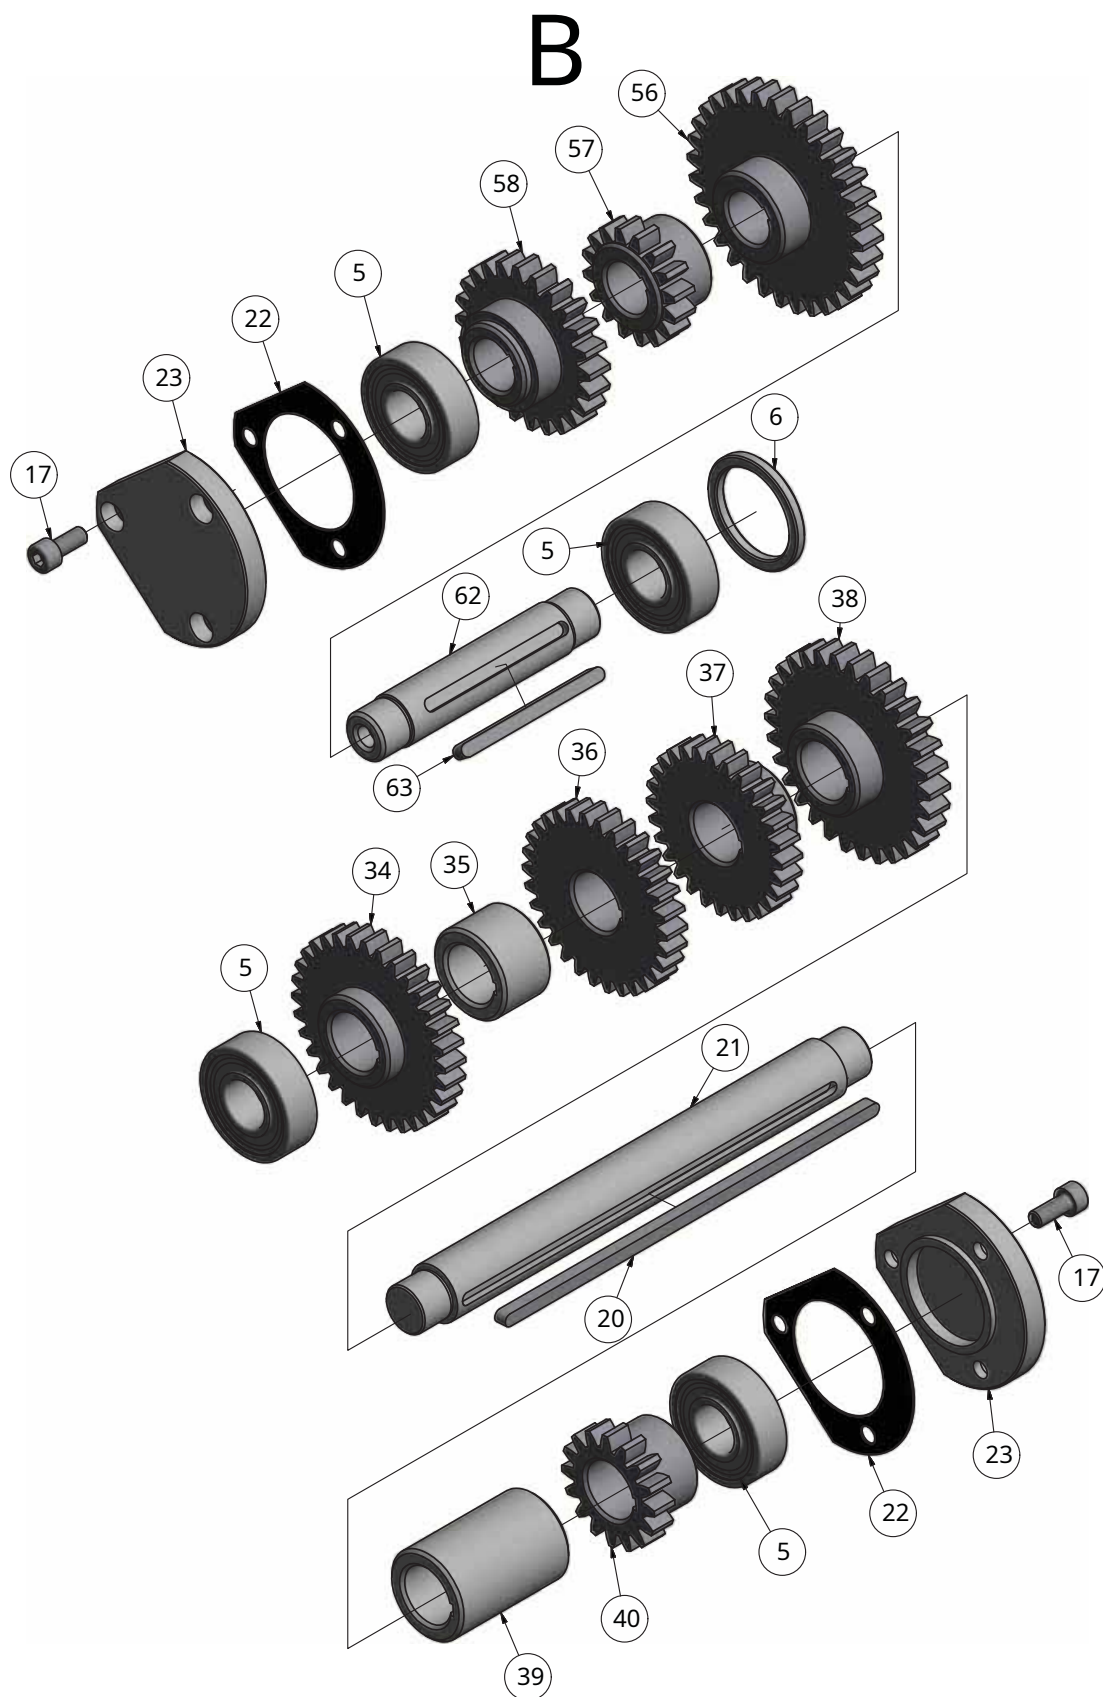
Vorschubgetriebe 4-6 - Engranaje de alimentación 4-6
